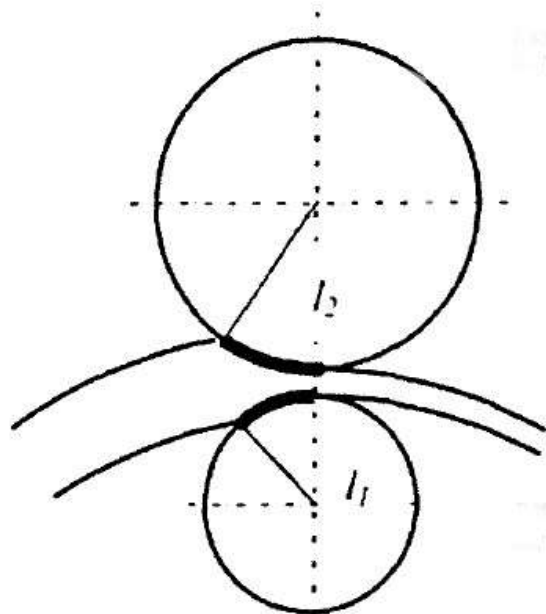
зоны контакта заготовки кольца с главным и дорновым валками
